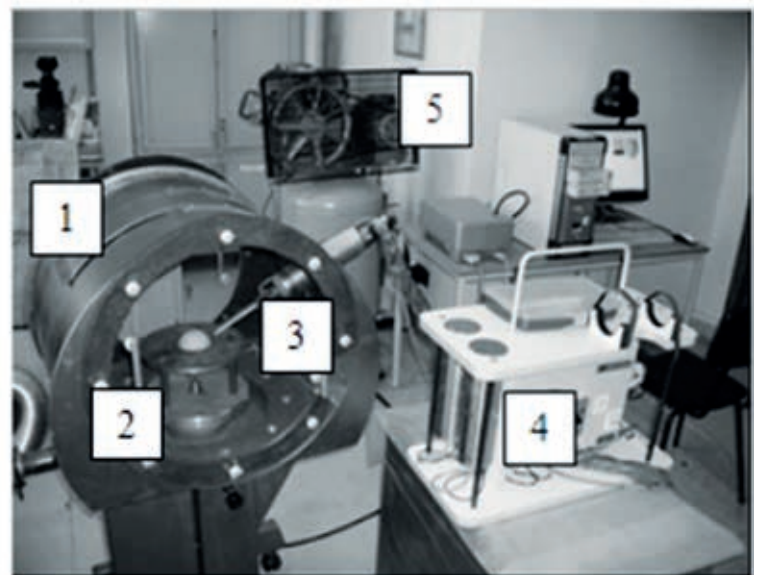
Полуавтоматическая установка нанесения покрытий методом ХГН: 1 — камера; 2 — манипулятор с образцами; 3 — сверхзвуковое сопло; 4 — порошковый питатель; 5 — компрессор
